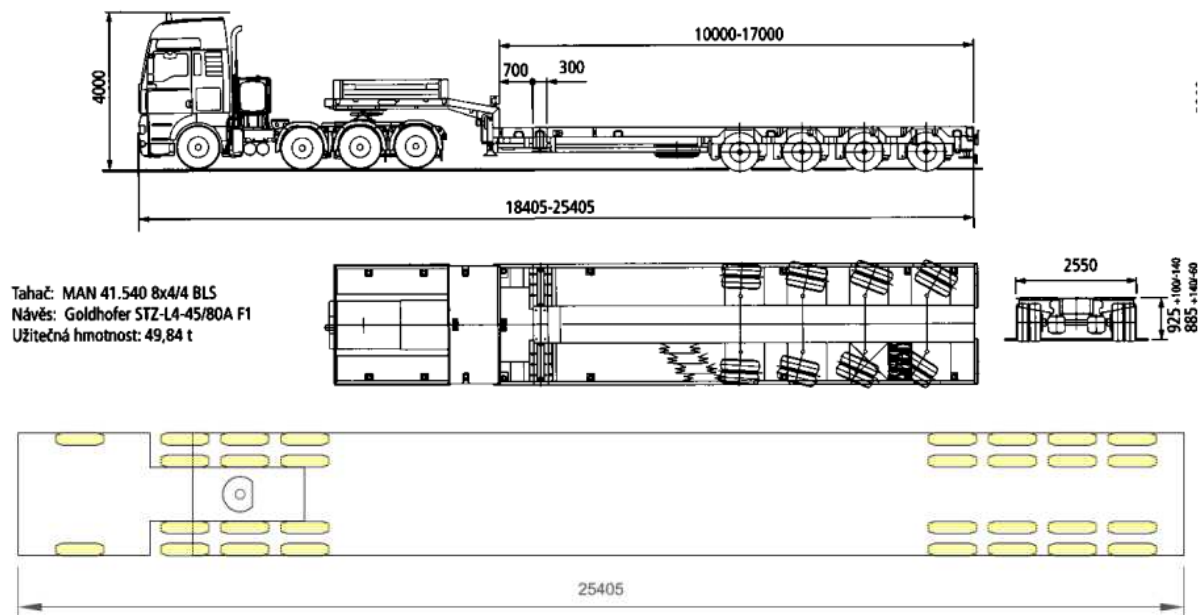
Doprava pilotovací soupravy, zdroj: [3]
